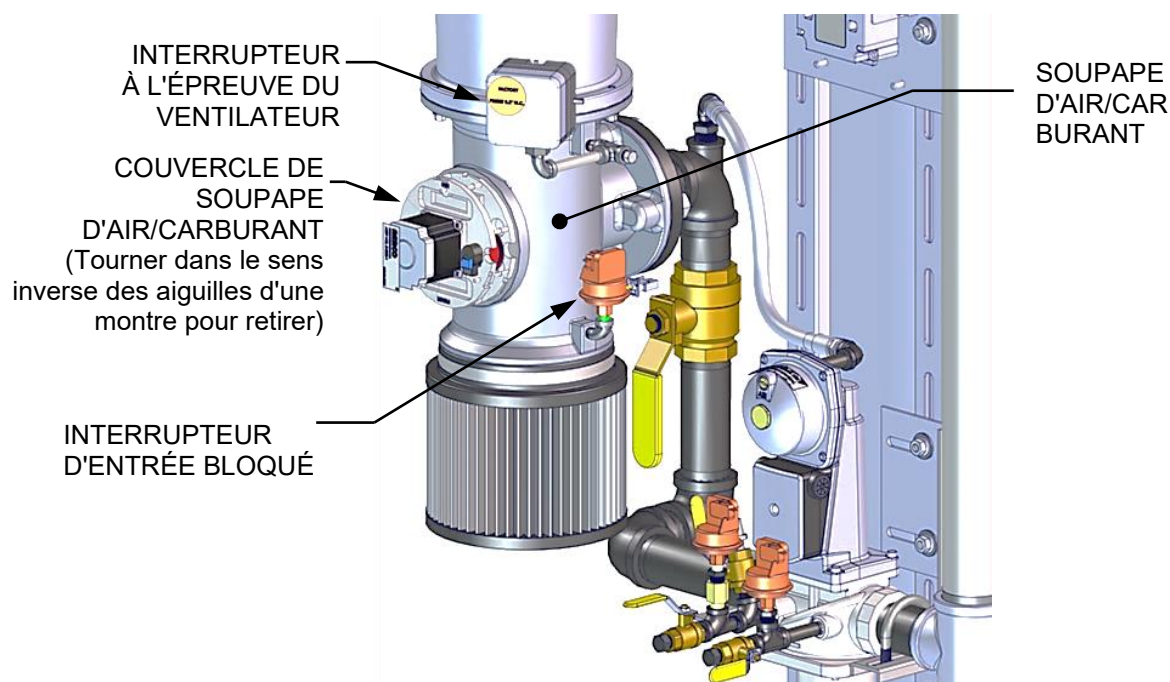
Emplacement du couvercle de soupape d'air et de carburant – BMK1500 illustré
